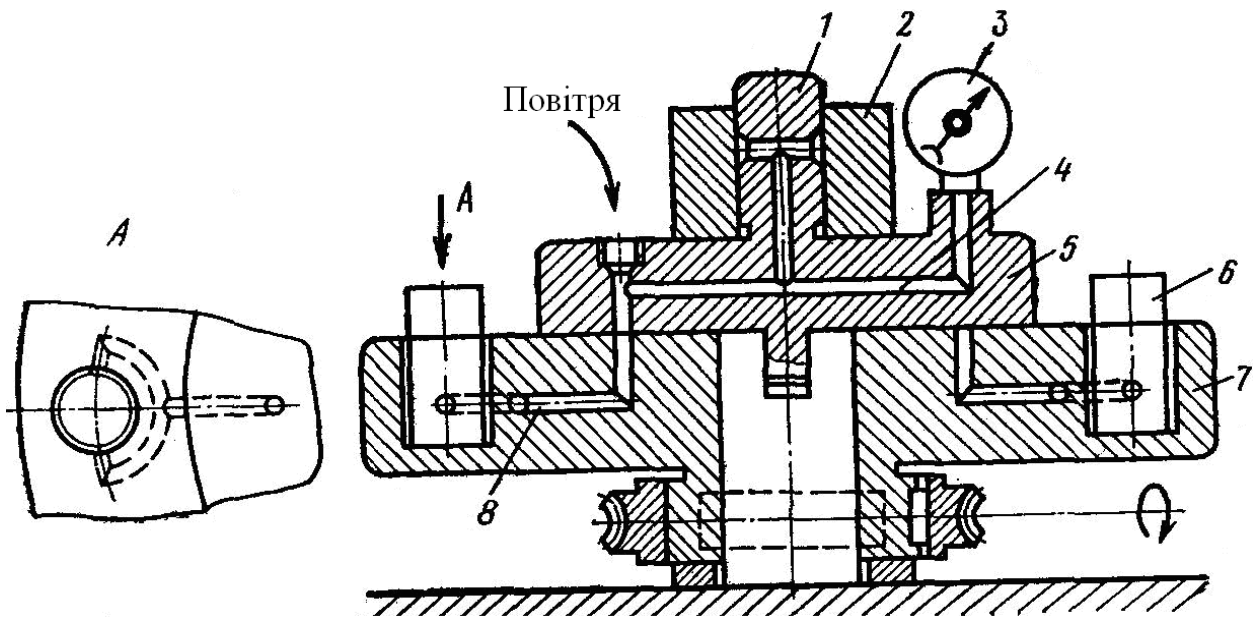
Схема пристрою для механізації підбору парних деталей:
